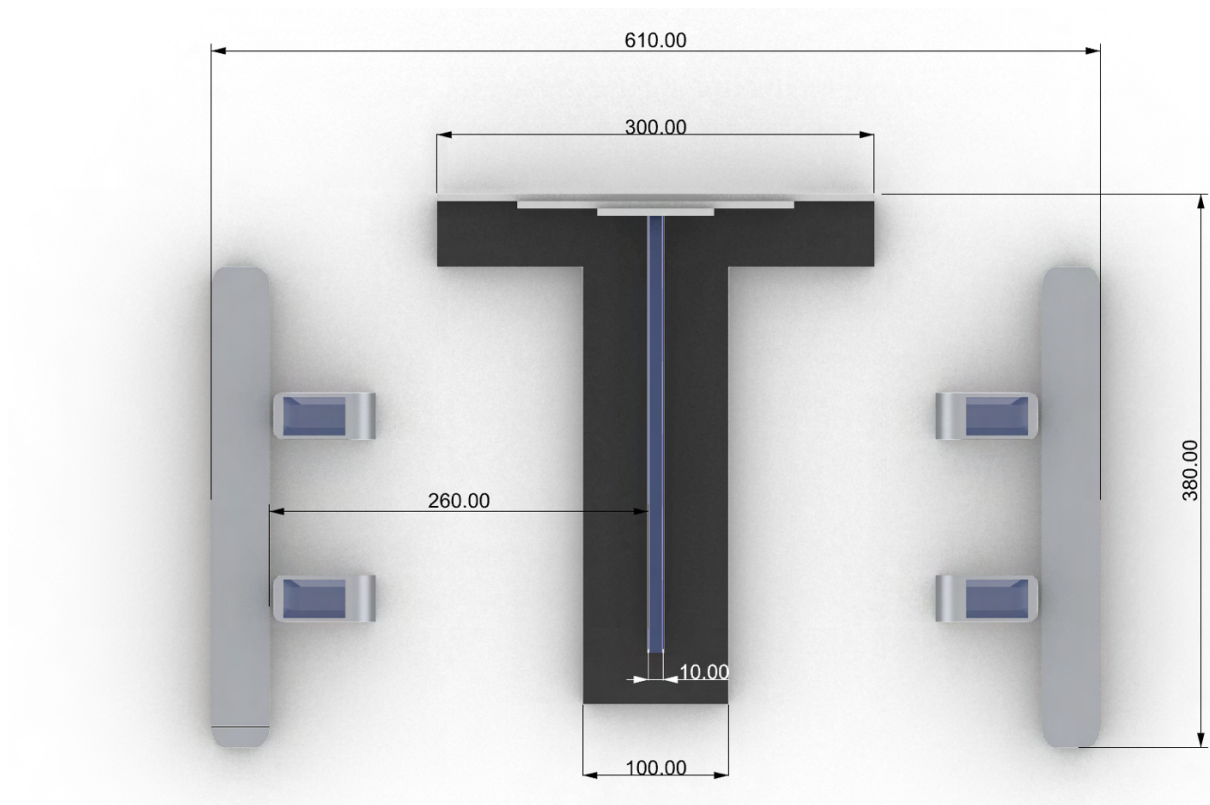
Vista dall'alto con l'ingombro complessivo dell'allestimento
